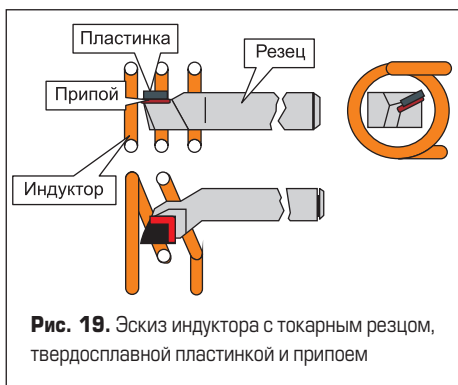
Эскиз индуктора с токарным резцом, твердосплавной пластиной и припоем
